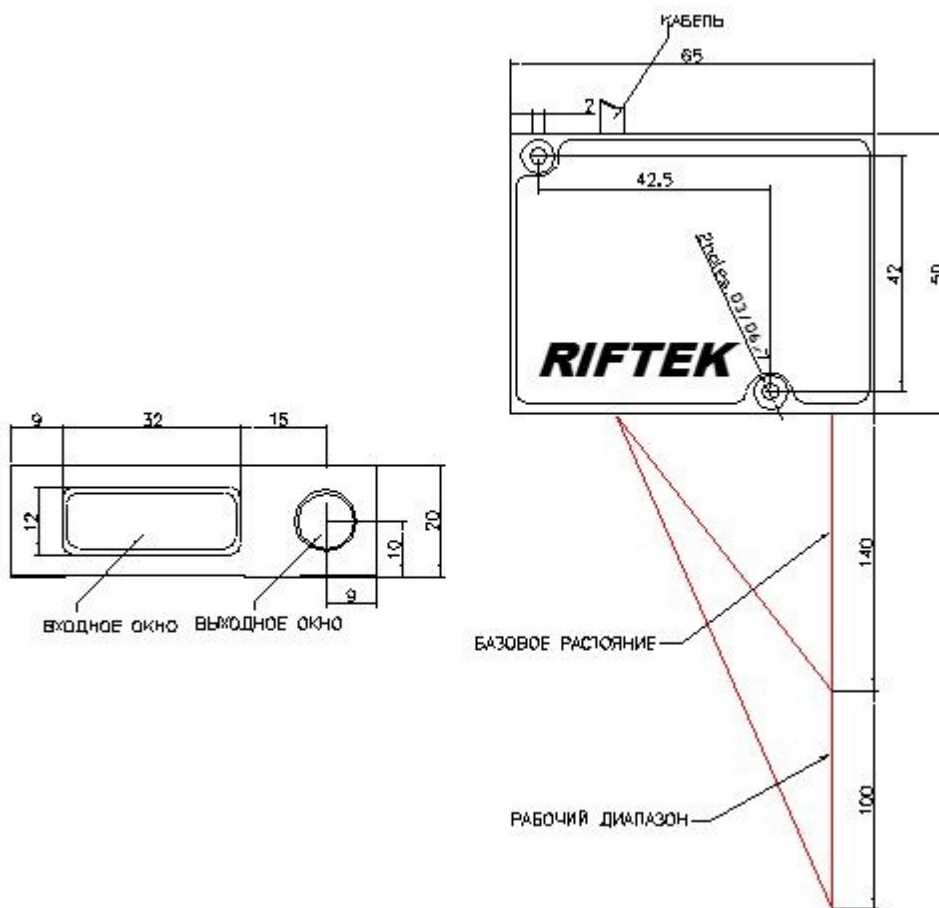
Габаритные и установочные размеры датчика РФ603
